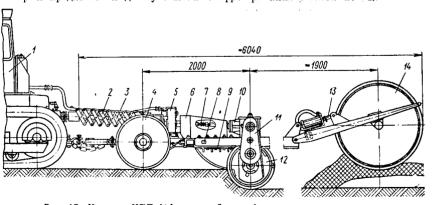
Машина МТП-42А для глубокого фрезерования кустарника:
